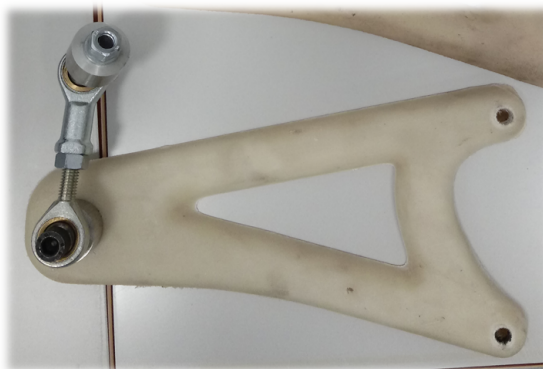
Prototipo de estribo fabricado y listo para ser ensayado.
